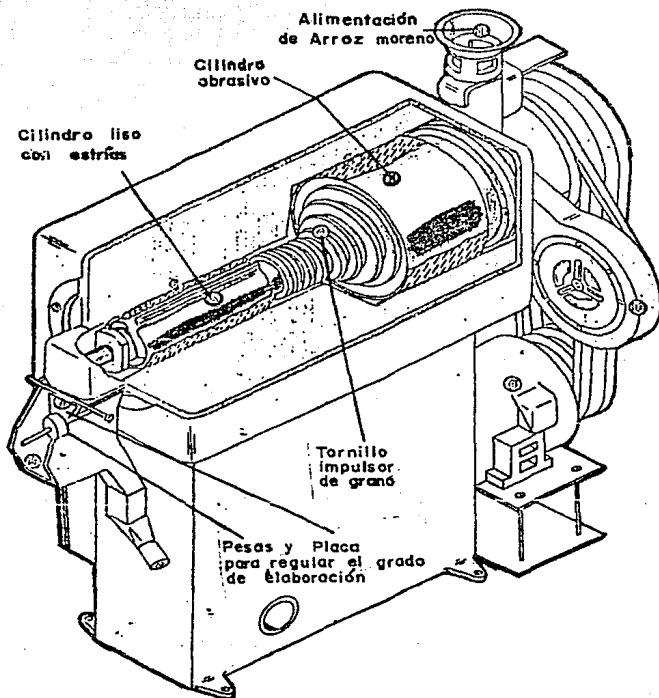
Blanqueadora de Cilindro Mixto. (3)
